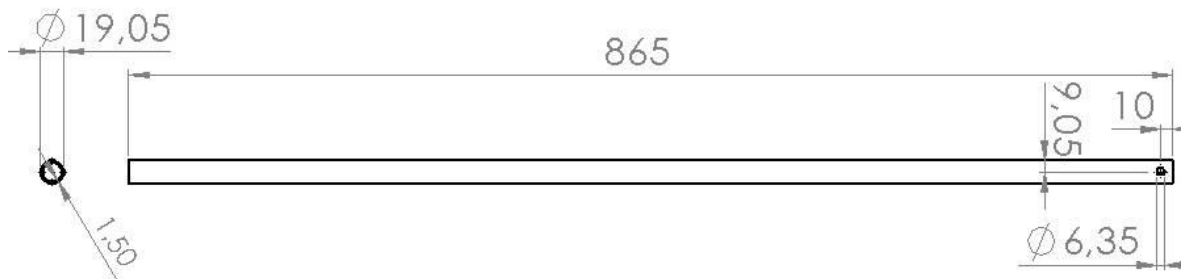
14 Plano lateral inferior de popa
